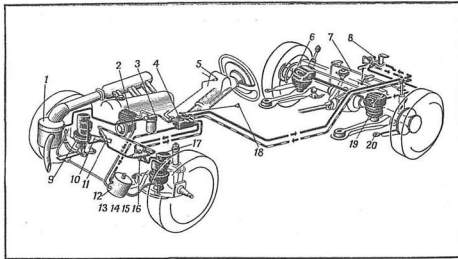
Пневматическая подвеска: 1 — воздушный фильтр, 2 — компрессор, 3 — противоморозное приспособление, 4 — клапанная коробка, 5 — сигнальная лампочка на щитке приборов в кабине, 6 — воздушная камера, 7 — задний торсион, 8 — задний клапан регулировки уровня, 9 — передний правый мост, 10 — регулирующая тяга, 11 — передний правый клапан регулировки уровня, 12 — обратный клапан, 13 — ресивер, 14 — спускной клапан, 15 — наполнительный клапан, 16 — передний левый клапан регулировки уровня, 17 — воздушная камера, 18 — выкатная кнопка клапанной коробки, 19 — задний левый мост, 20 — опорный тормозной рычаг.
